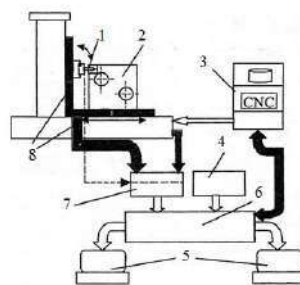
Схема мониторинга с индикатором контакта: 1 - индикатор контакта; 2 - заготовка (деталь); 3 - пульт управления; 4 - устройство ввода информации; 5 - терминалы; 6 - головной компьютер управления; 7 - счетчик; 8 - импульсные линейки
